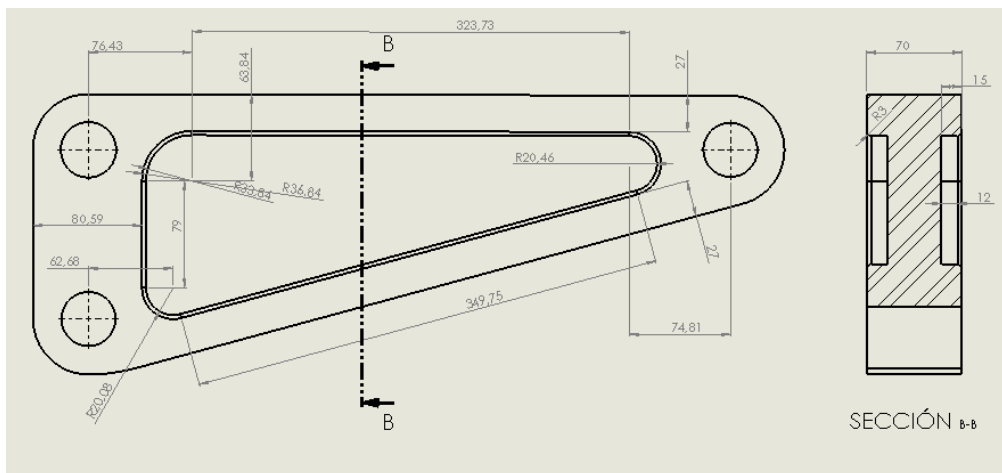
Plano barra EFD rebajada en SolidWorks.
